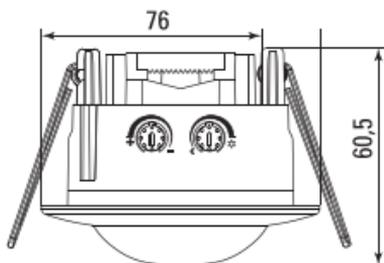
Габаритные и установочные размеры датчика MS-100
